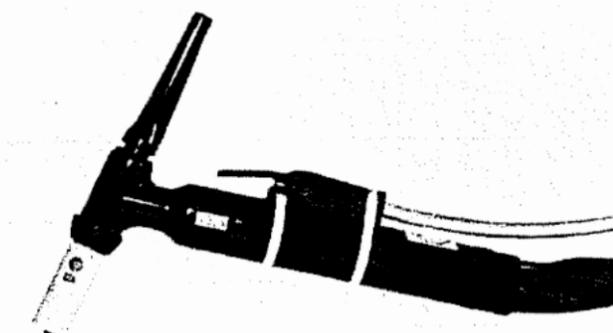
Горелка для Аргонодуговой сварки стандартного типа
